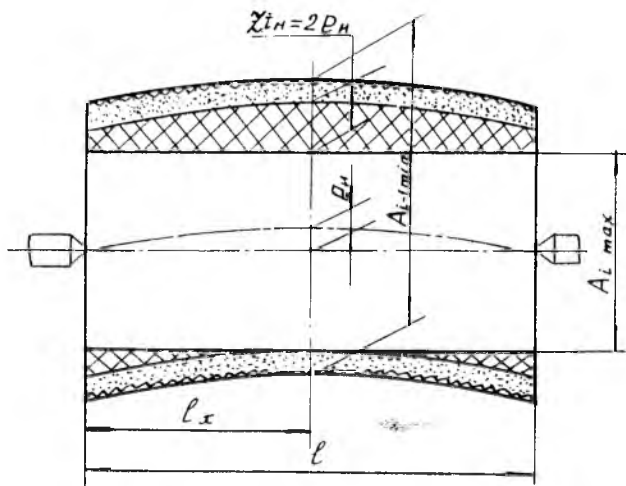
Неравномерность припуска в результате коробления оси заготовки
